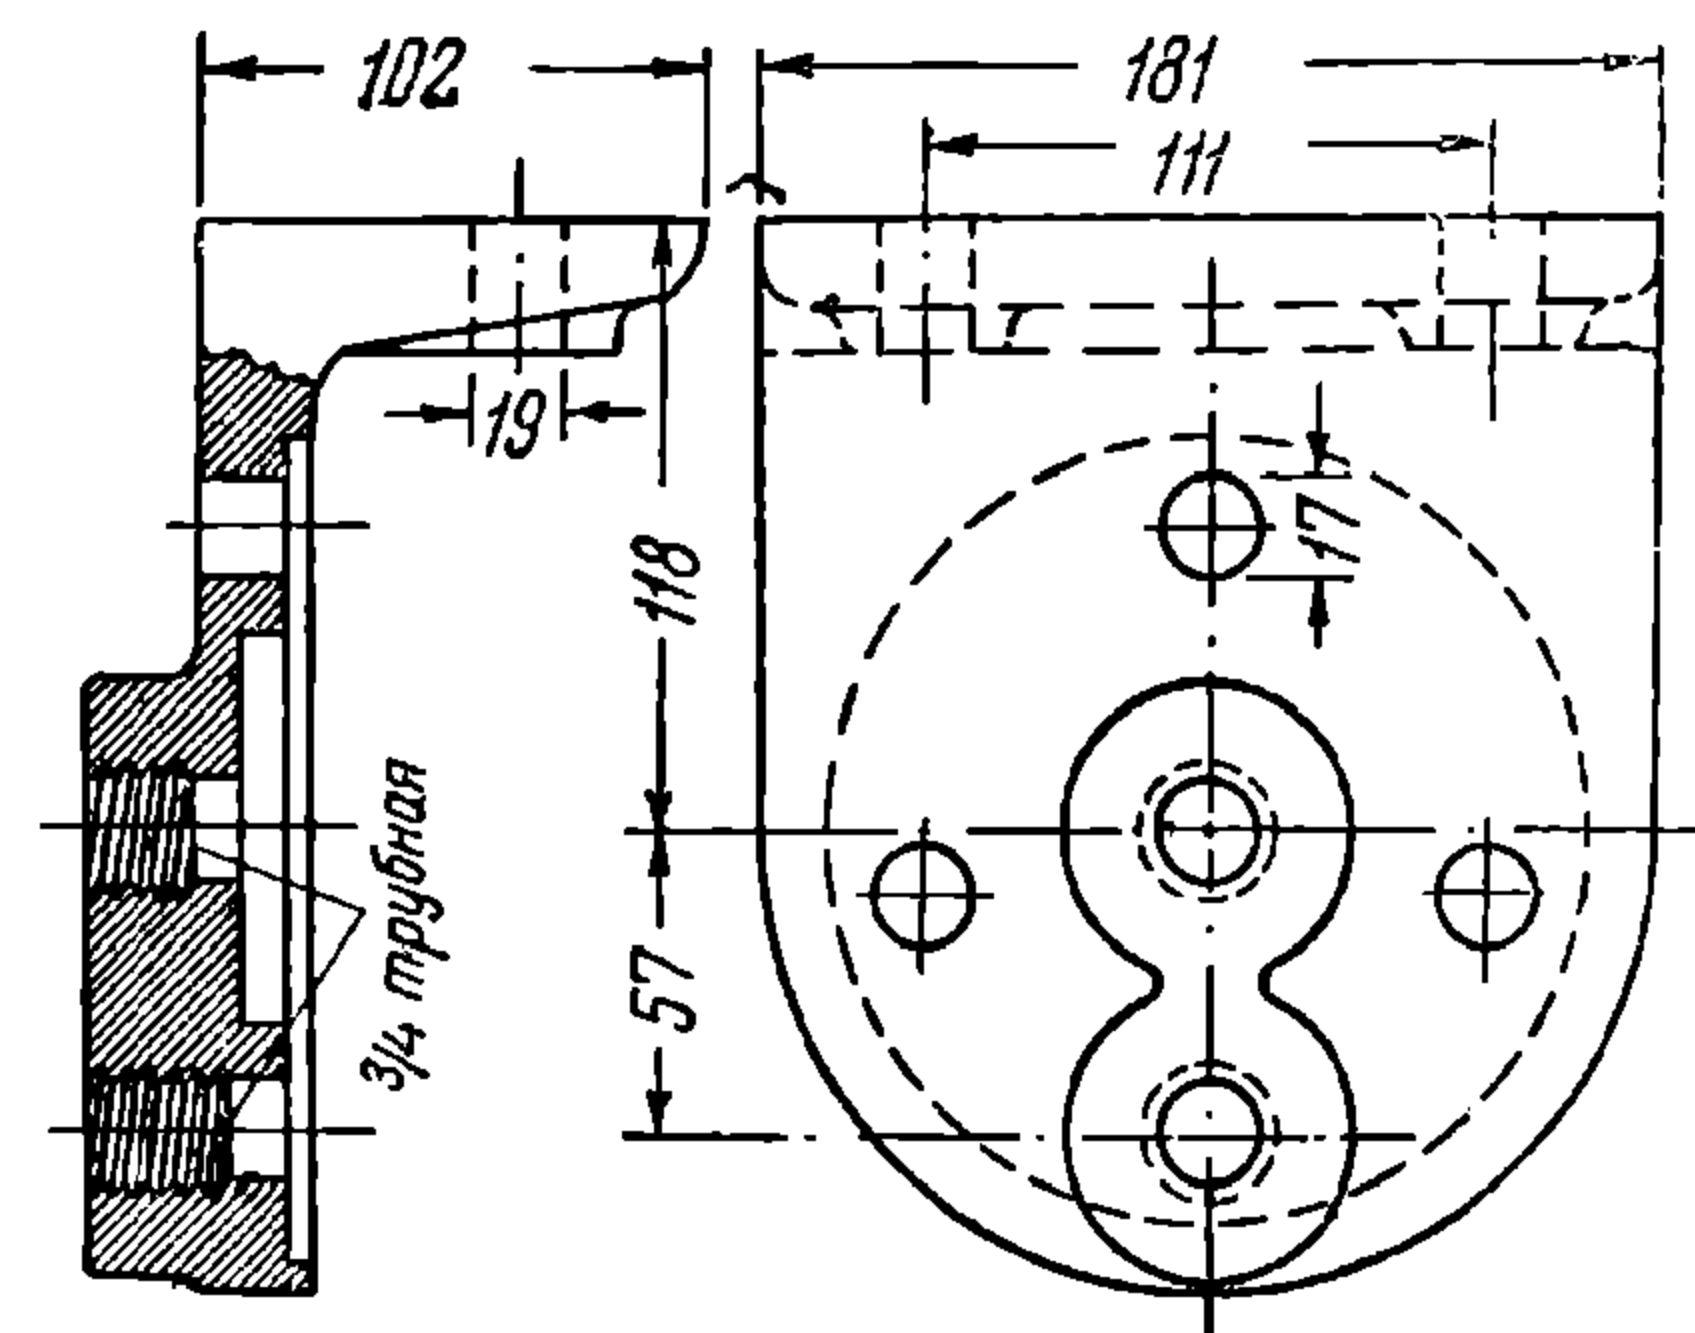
Часть диска поршня и корпуса тормозного цилиндра.
